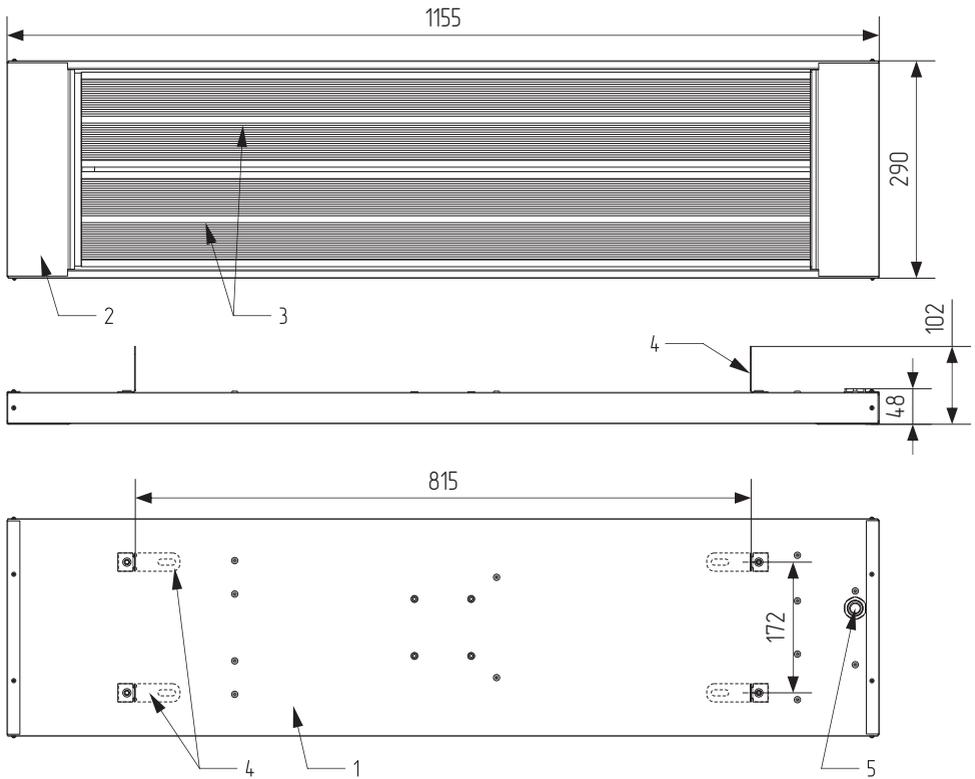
Габаритный чертёж и элементы конструкции инфракрасного обогревателя М-1500MI-34.
